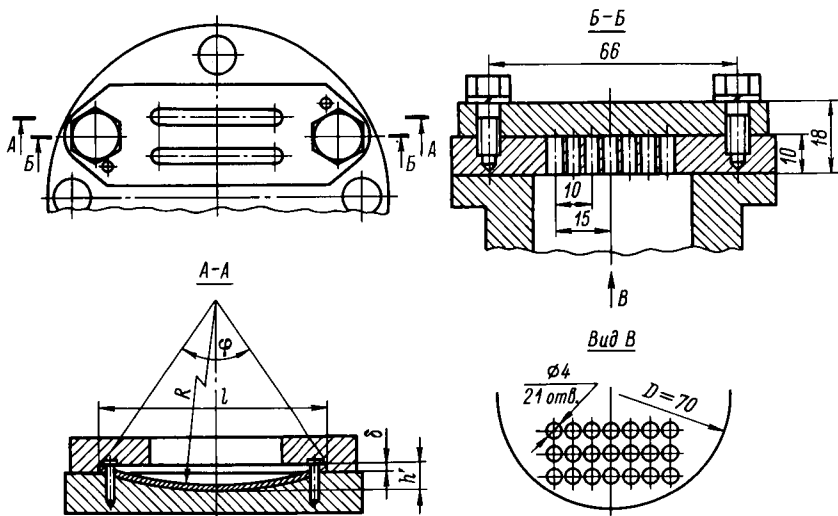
Ленточный полосовой всасывающий клапан непрямоточного компрессора
